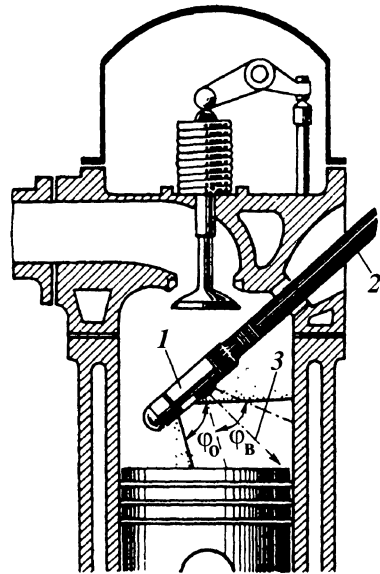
Схема проверки цилиндра двигателя через отверстие с помощью жесткого эндоскопа:
